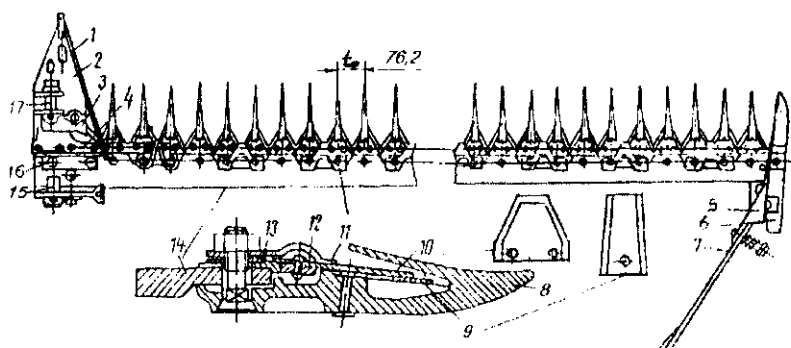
Сегментно-пальцевый режущий аппарат косилки КС-2.1: 1-делитель; 2-внутренний башмак; 3 и 16-передняя и задняя направляющие крышки головки ножа; 4-головка ножа; 5-наружный башмак; 6-опорный полз; 7-полевая доска; 8-палец; 9-противорежущая пластина (вкладыш); 10-сегмент; 11-прижимная ланка; 12-спинка ножа; 13-пластина трения; 14-пальцевый брус; 15 и 17-штыри для навешивания аппарата к раме косилки.
